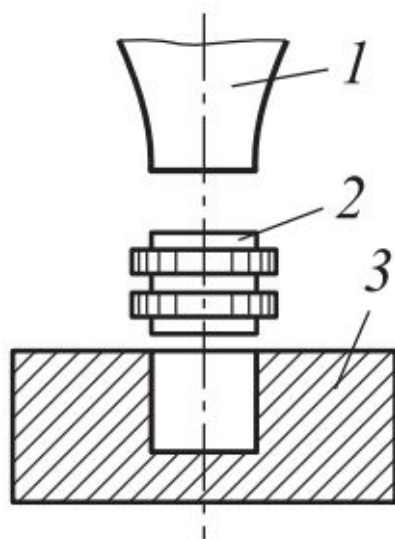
Схема запрессовки металлической детали в пластиковую:
